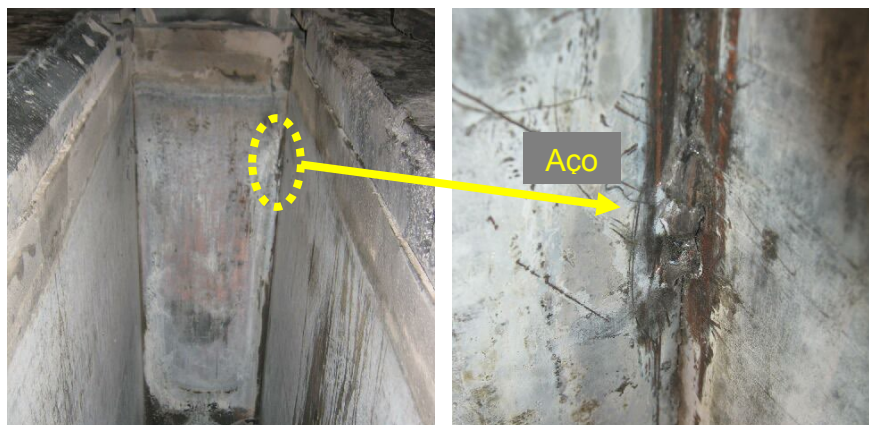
Face estreita de molde (à esquerda) com detalhe da penetração de aço entre as faces larga e estreita de molde (à direita).
